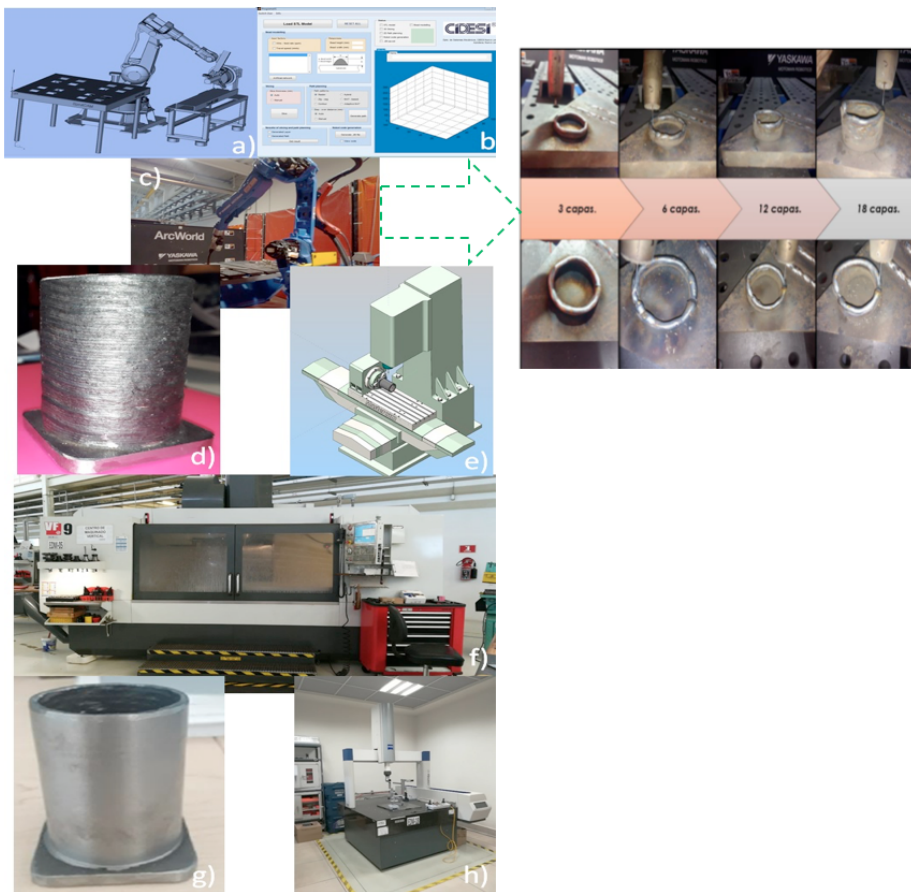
Imágenes que indican: a) modelación, b) parametrización, c) soldadura con celda de manufactura, d) pieza soldada, e) modelación para maquinado, f) maquinado, g) parte final, y h) medición de pieza construida a base de acumulación de soldadura. Fotografías cortesía de CIDESI Sede Nuevo León y Estado de México
